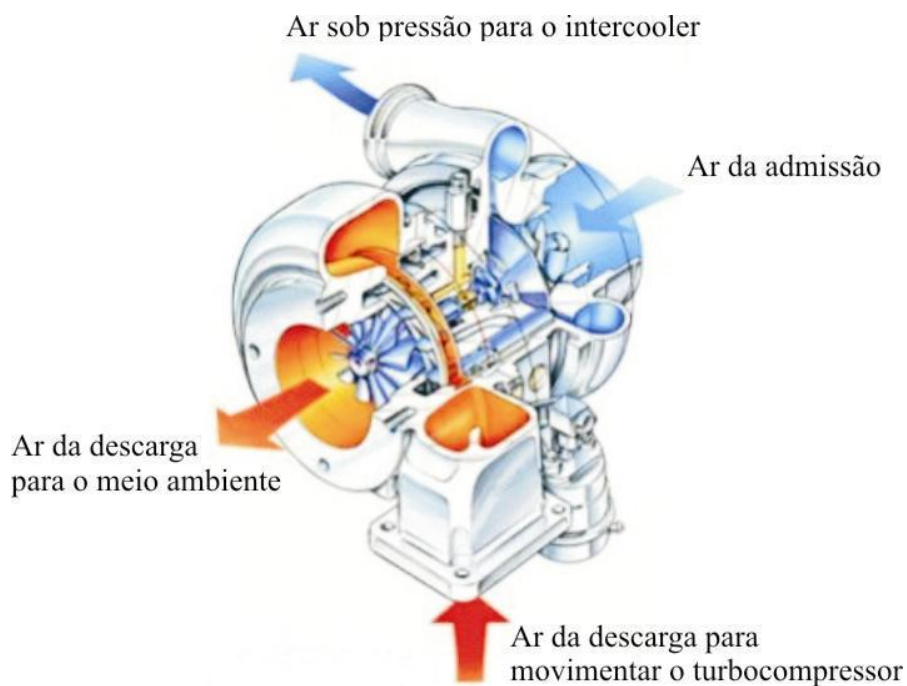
Turbocompressor, turbina, turbocharger, turboalimentador ou turbo.
